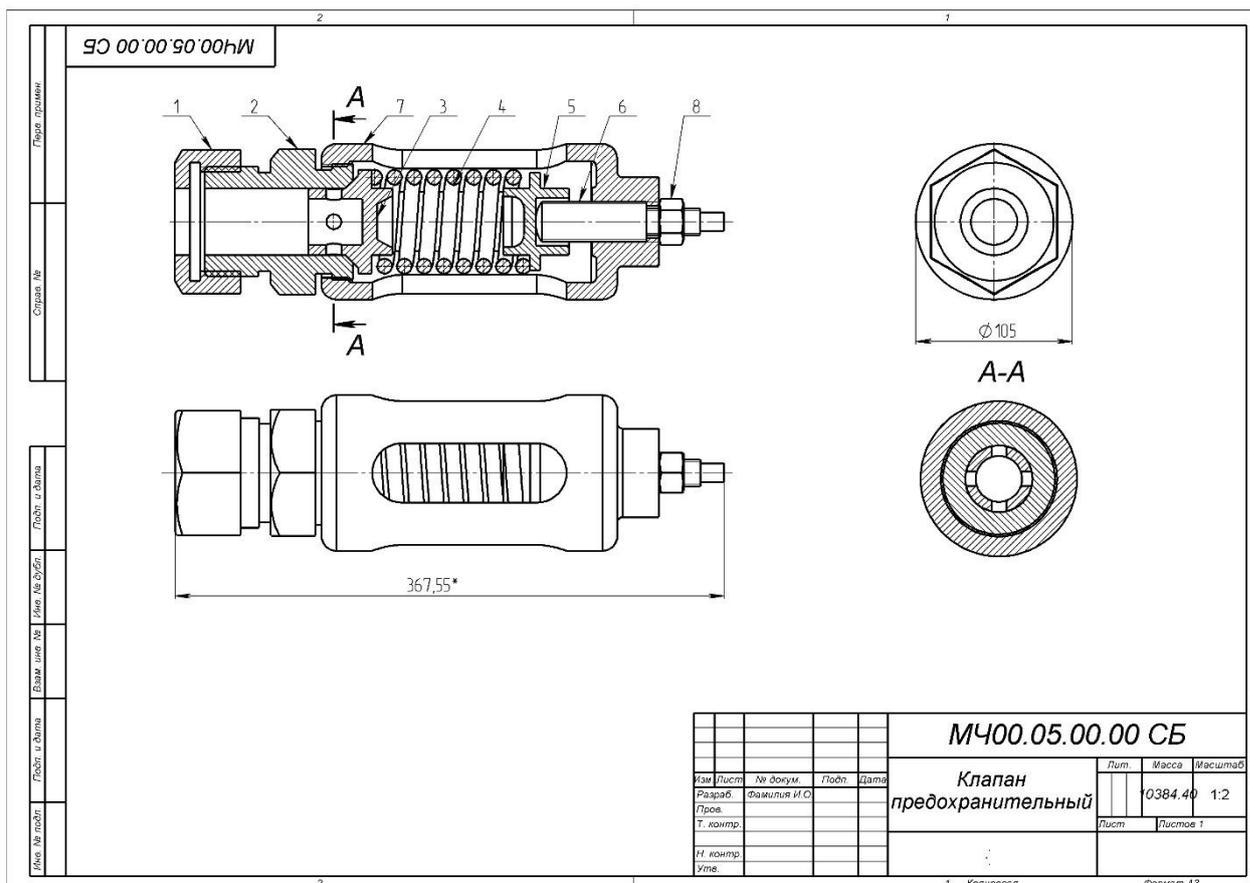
Сборочный чертёж механизма «Клапан предохранительный» созданный в SolidWorks
